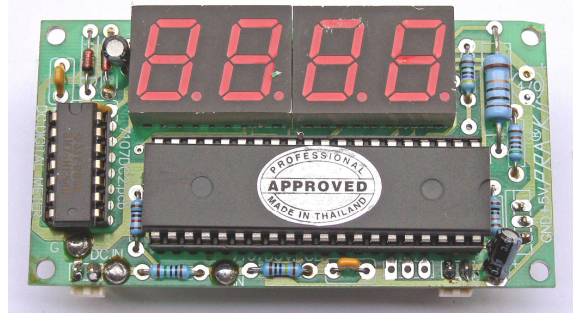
ลายปริ้นท์แบบ 2 หน้า plate thru hole
